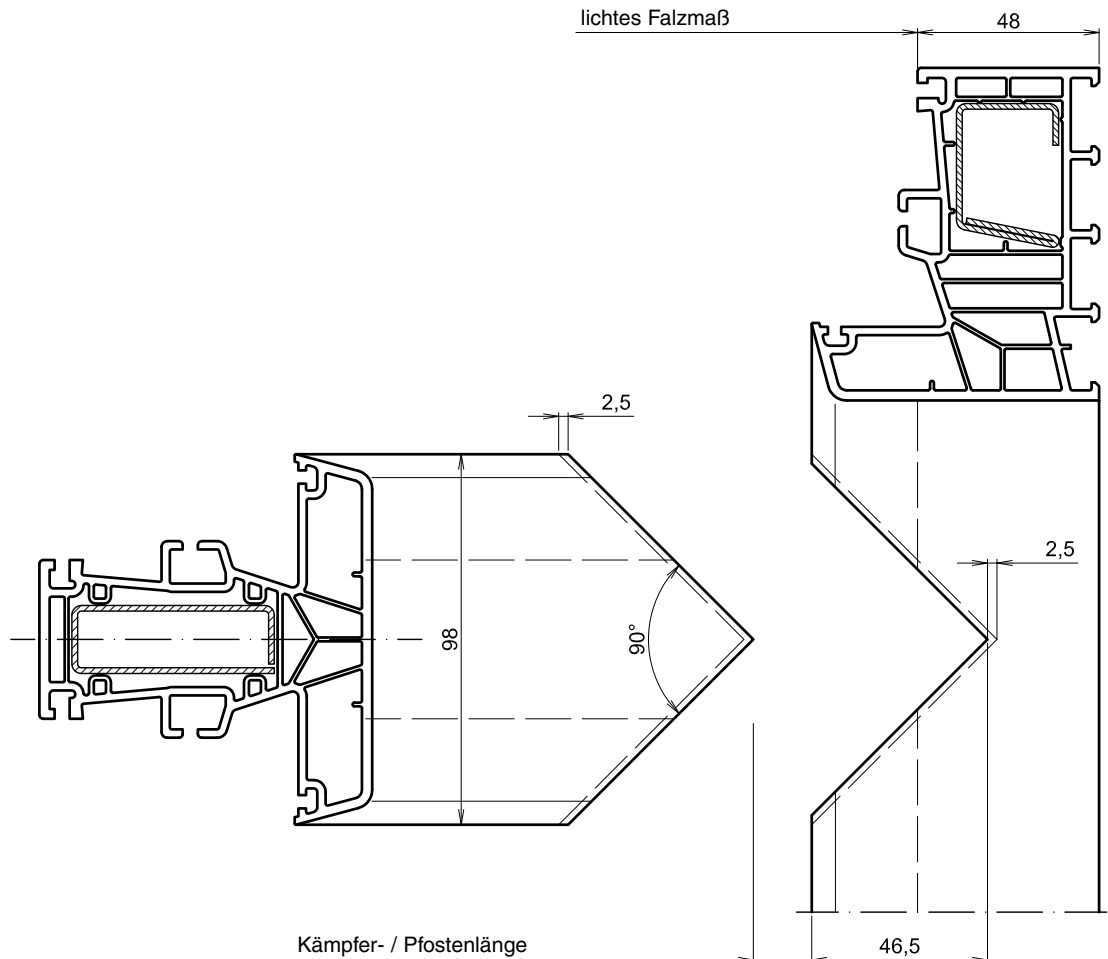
Einschweißmaße am Beispiel 6221.1
